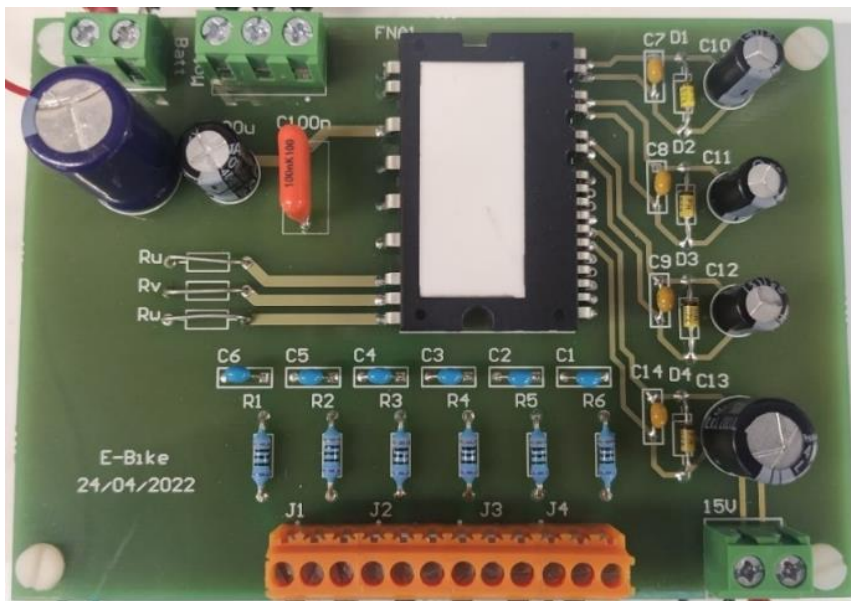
PCB de teste do circuito de potência soldada.
